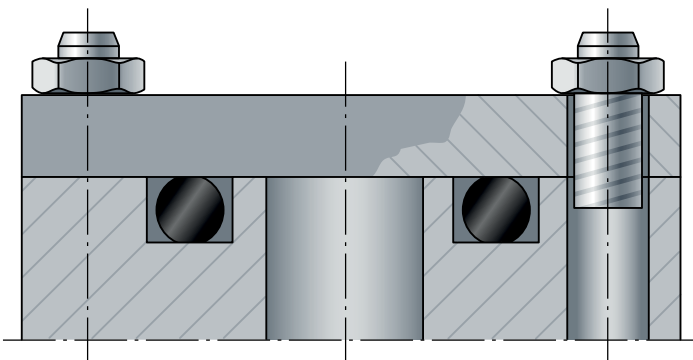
Flanschdichtung: O-Ring axial verpresst
